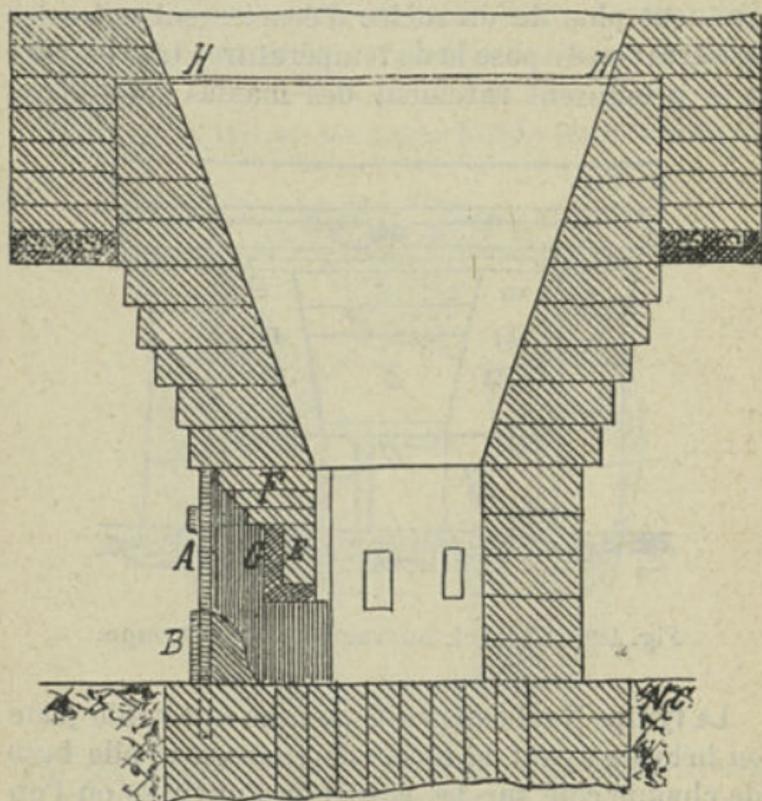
Creuset, ouvrage et étalages d'un haut fourneau.
